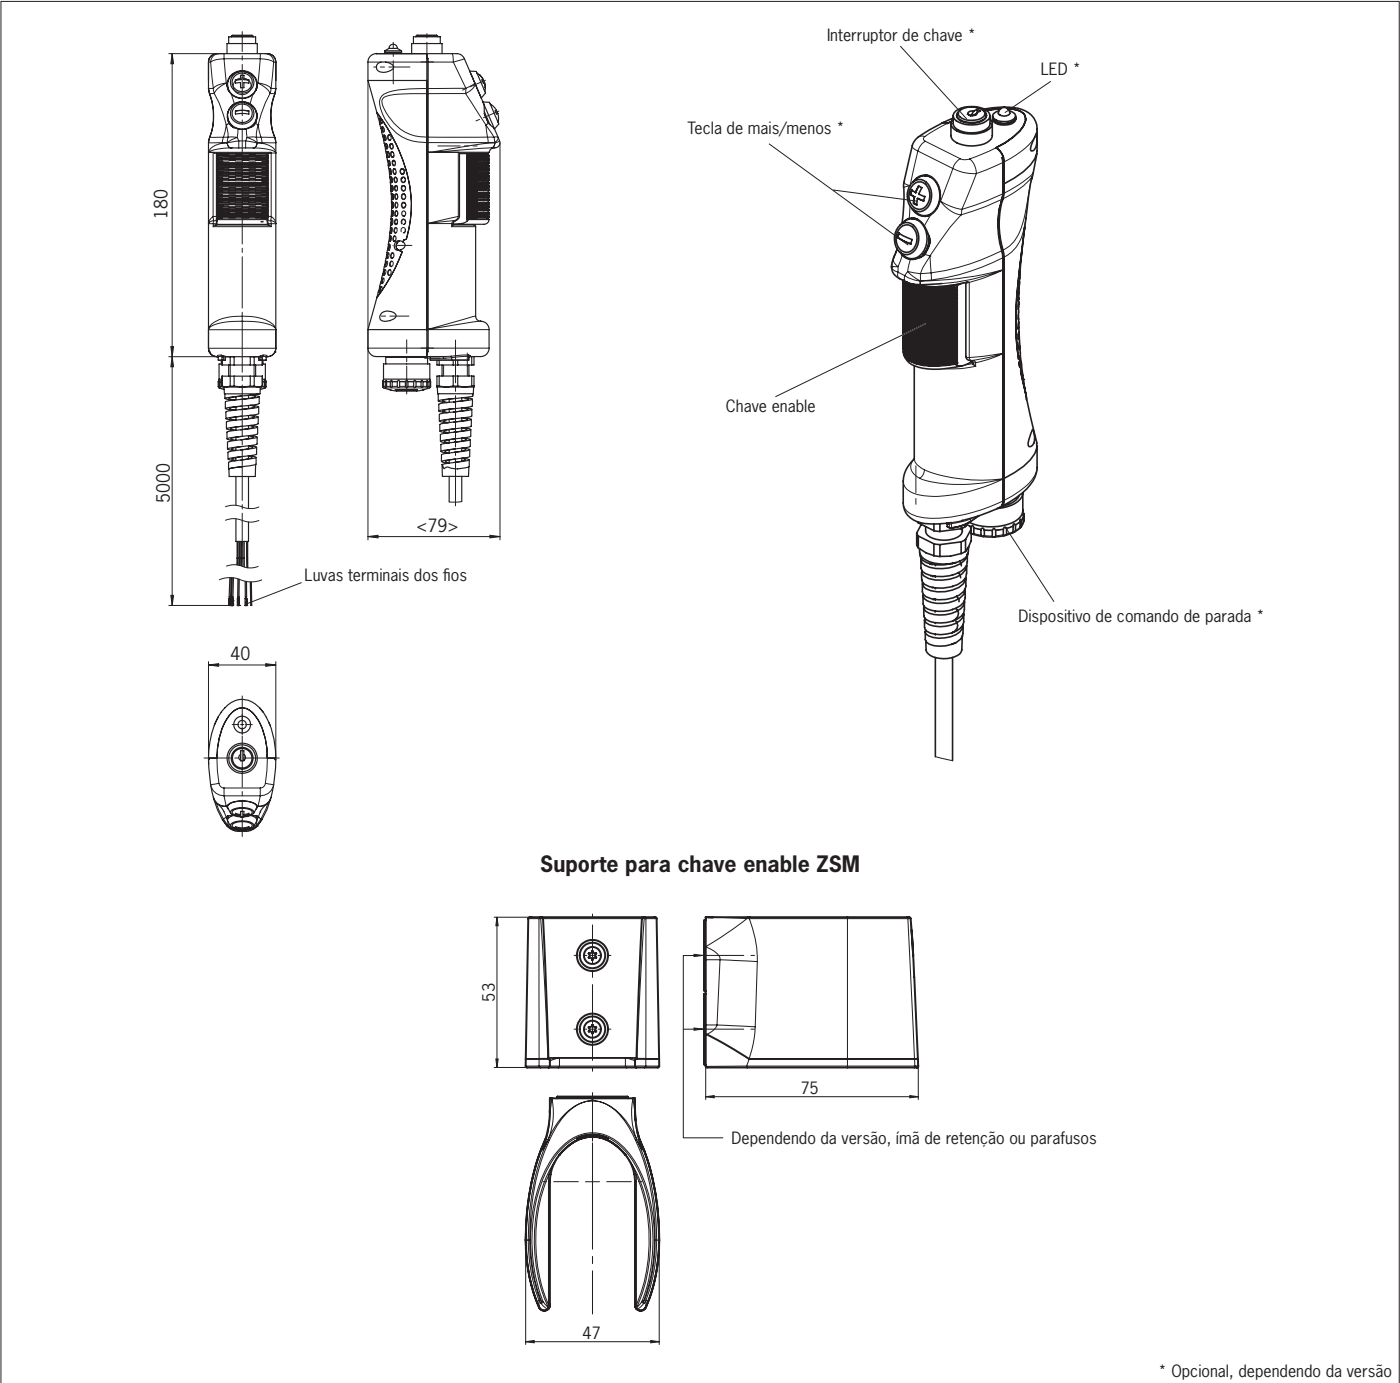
Desenho dimensional da chave enable ZSM e do suporte
